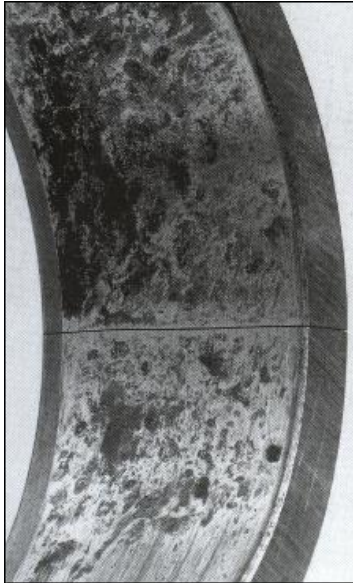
Aro interior de rodamiento de rodillos a rótula con corrosión de contacto y rotura transversal. La corrosión ha originado la rotura.
